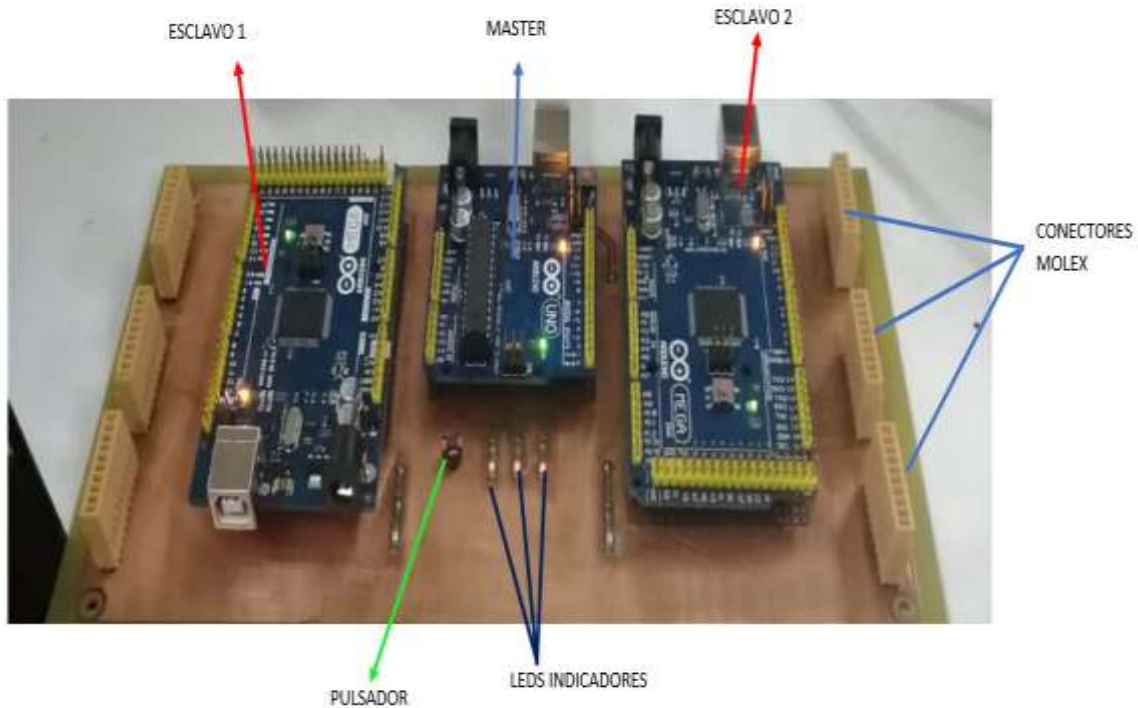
Tarjeta principal con elementos soldados
